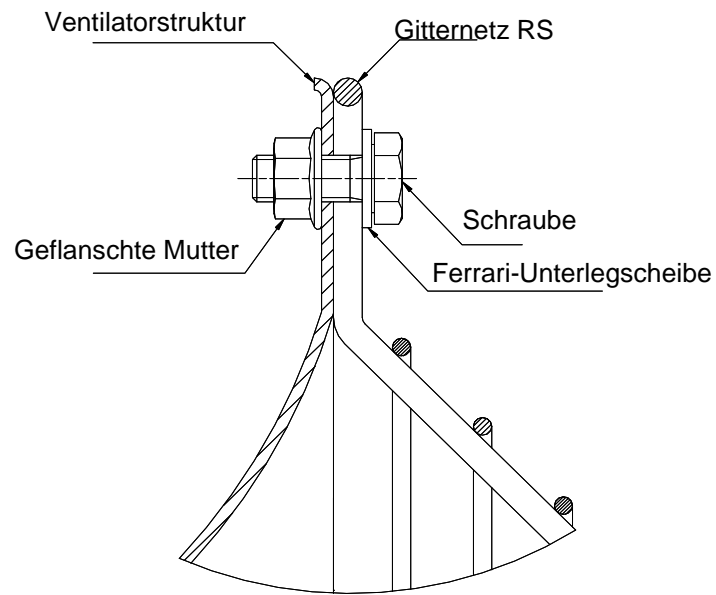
Montageplan der Schutzeinrichtung RS
